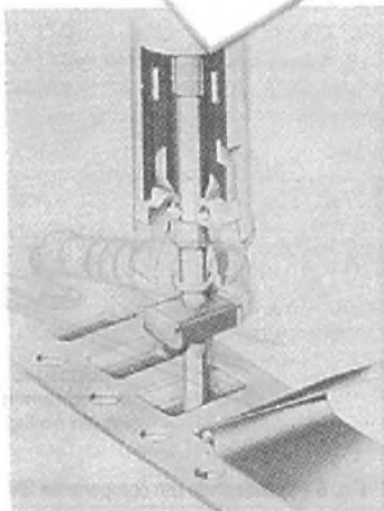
Máquina para montagem automática de placas com componentes SMD.
